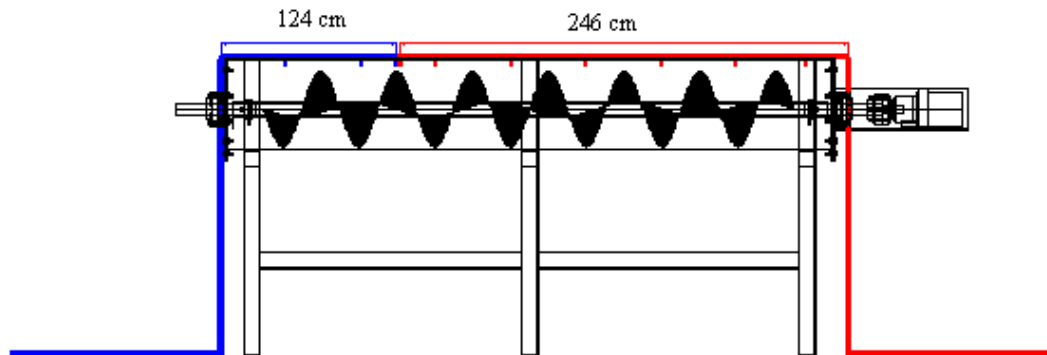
Tuberías del sistema de lavado. Fuente. Propia.
